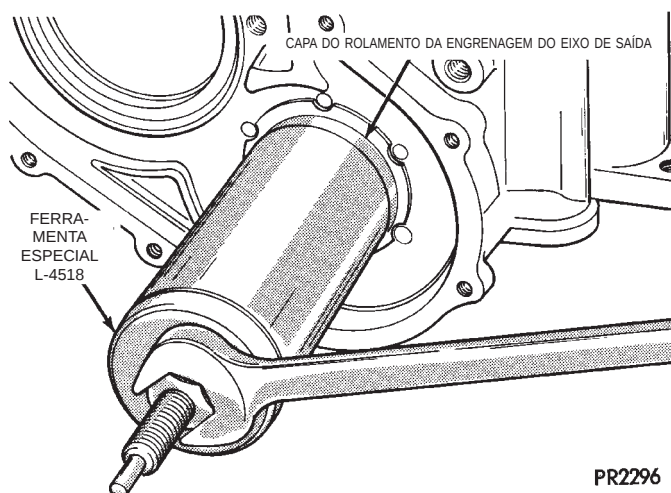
Remoção da Capa de Rolamento da Engrenagem do Eixo de Saída
